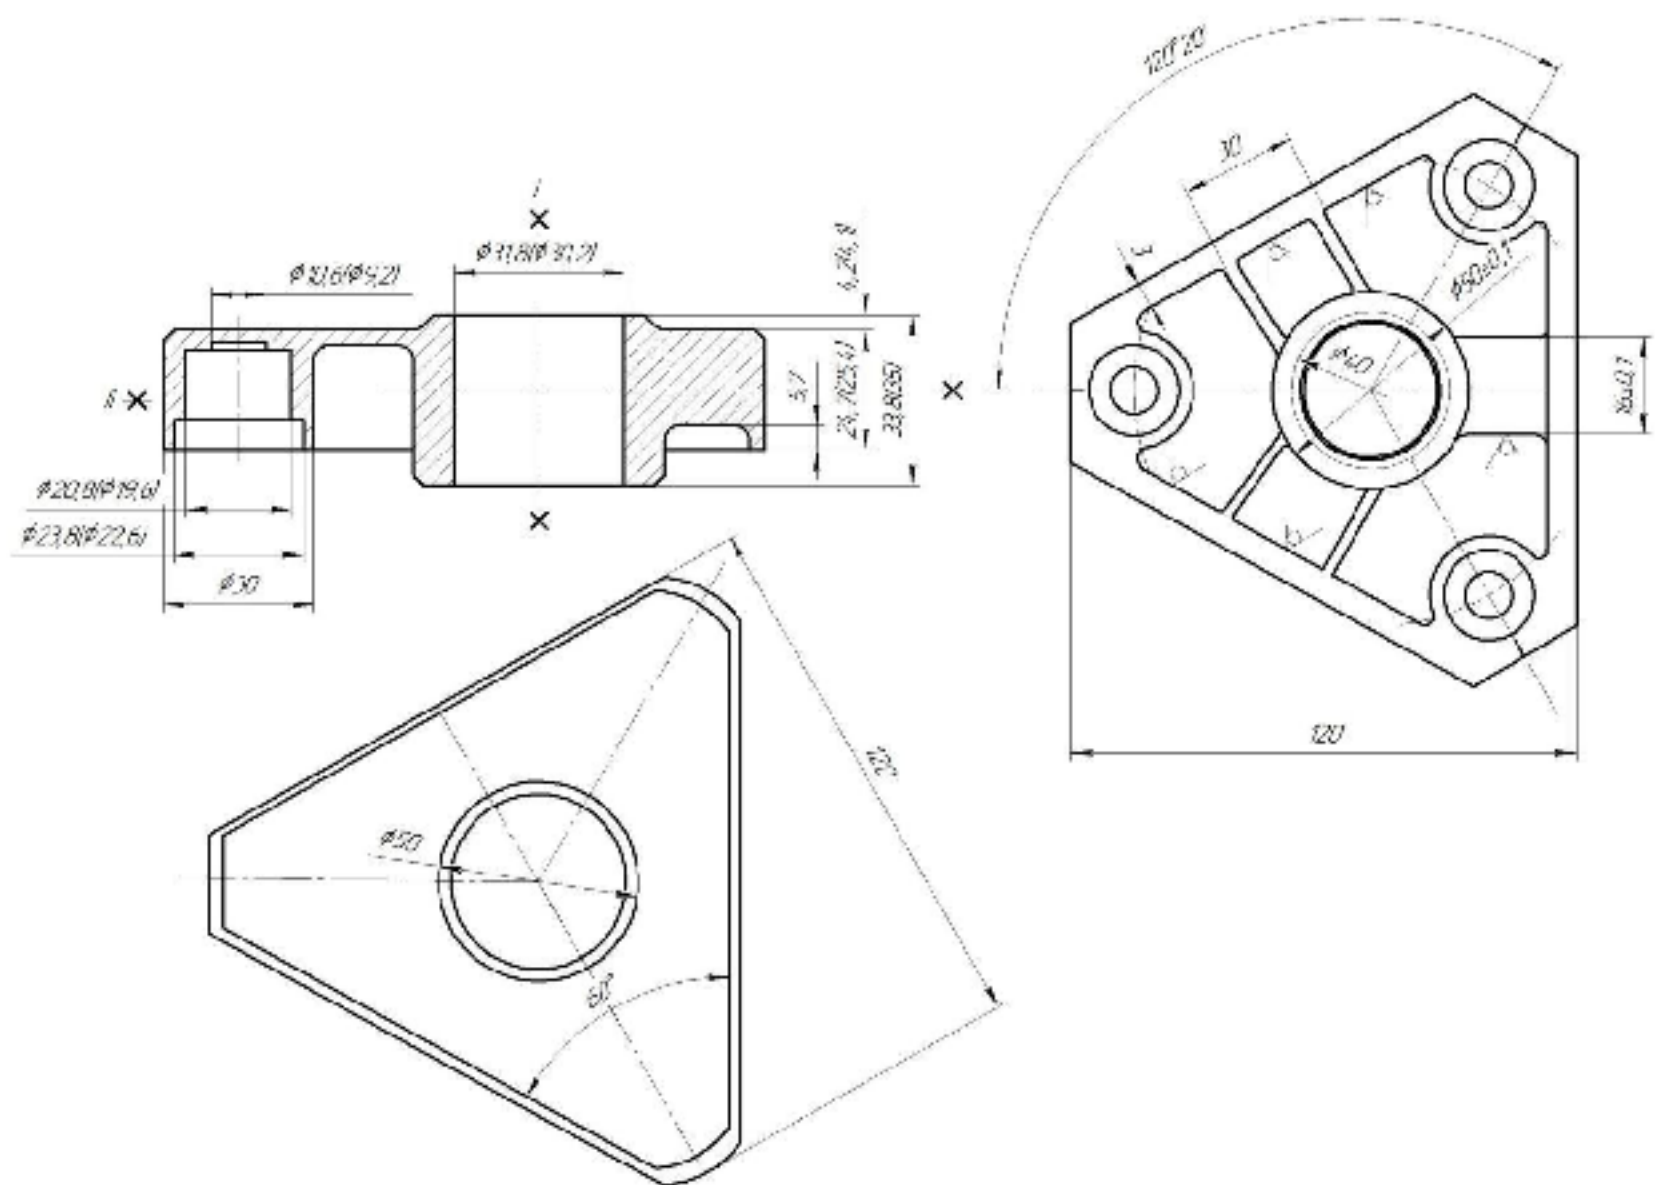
Ескіз заготовки при литті в кокіль (при литті під тиском розміри в дужках):
